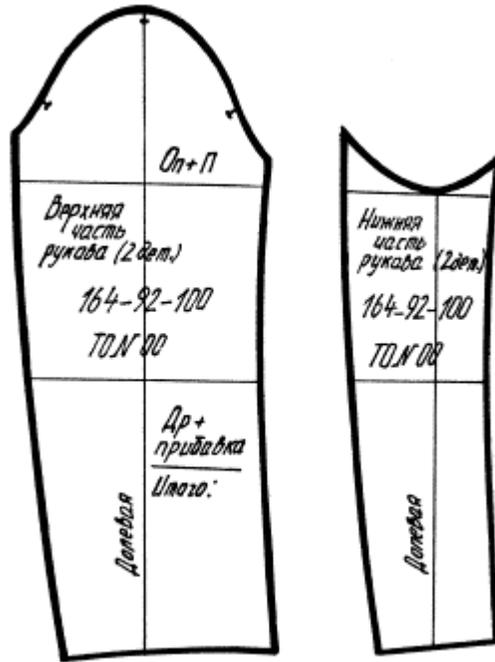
Рабочие чертежи лекал базовых конструкций
